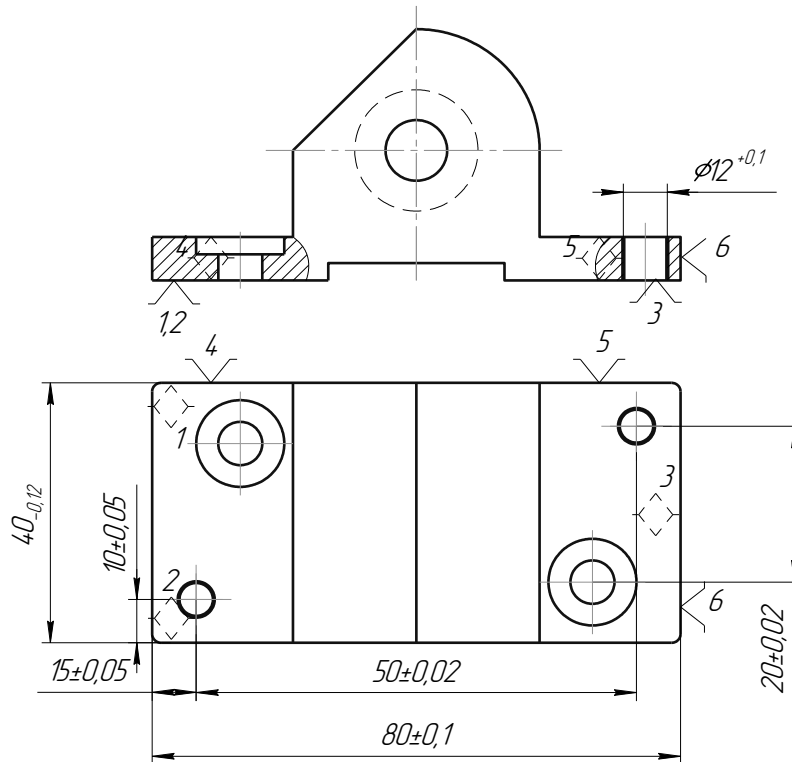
Схема базування деталі «Корпус підшипника»
